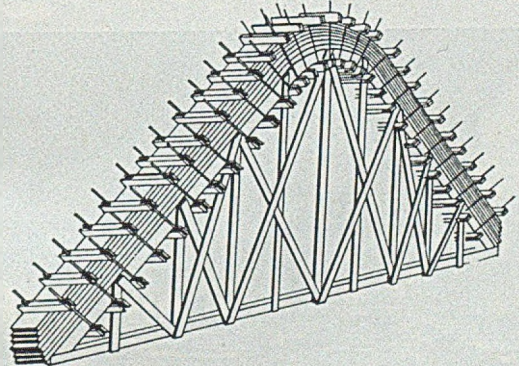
Stehender Zusammenbau eines gekrümmten Bauelementes mit Lehre und Klammern.
